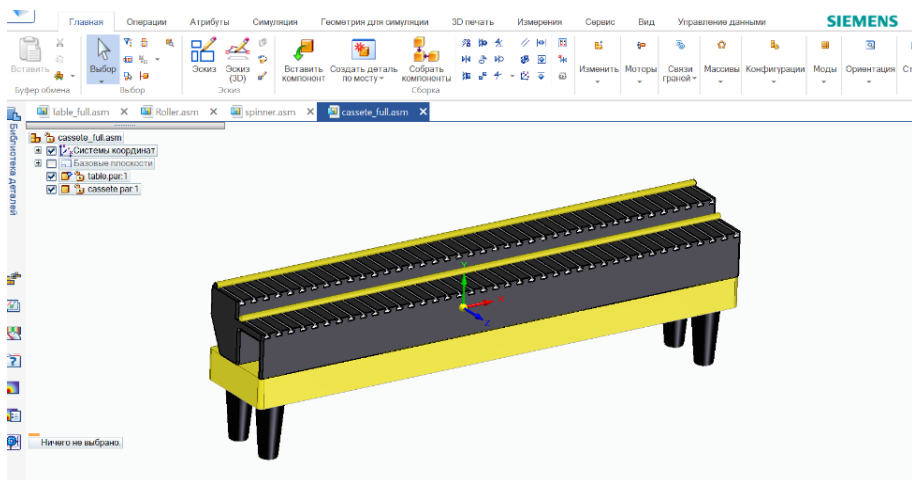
Подставка с кассетными двухъярусными питателями для обрезков лент установщика SMP-330.
